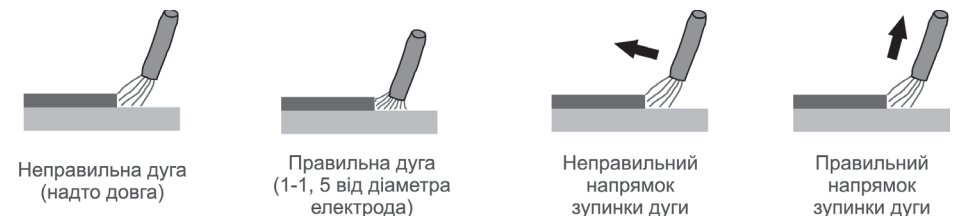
Відстань розташування електрода із покриттям до деталі під час ручного дугового зварювання («ММА»).
